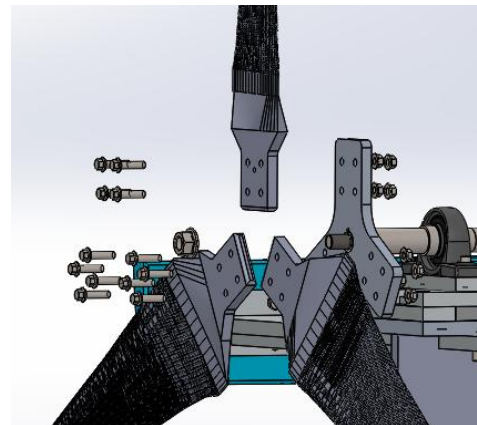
21. Detalle del montaje. Fuente: diseño propio.
